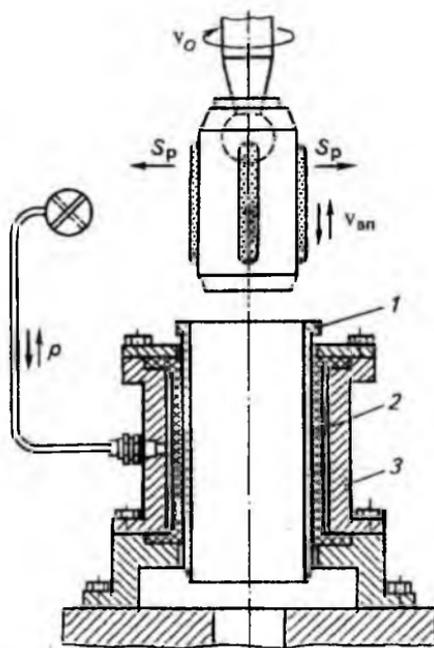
Схема приспособления для крепления гильзы при хонинговании:
